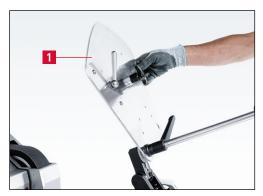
Schleifplatte nach hinten in die Verdrehsicherung geschwenkt
